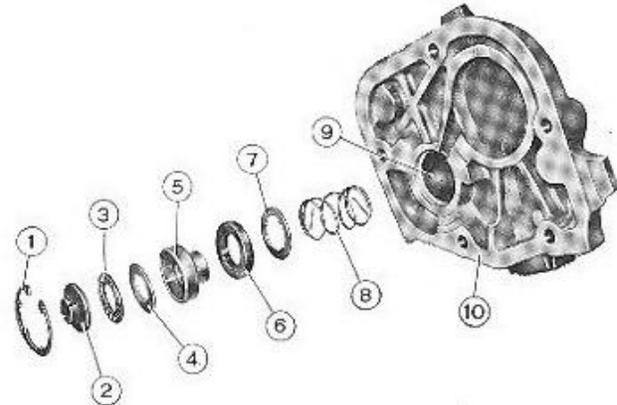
Arbeitszylinder zur Betätigung der hydraulischen Ausrückvorrichtung.
